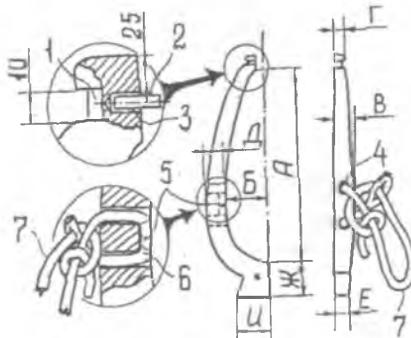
Клещи: 1 - канальчики для верхнего споя; 2 - шпинец-распорка; 3 - углубление для шпинец-распорки; 4 - отверстие для гужей; 5 - канавка для укладки петель гужа; 6 - петли гужа; 7 - гуж
